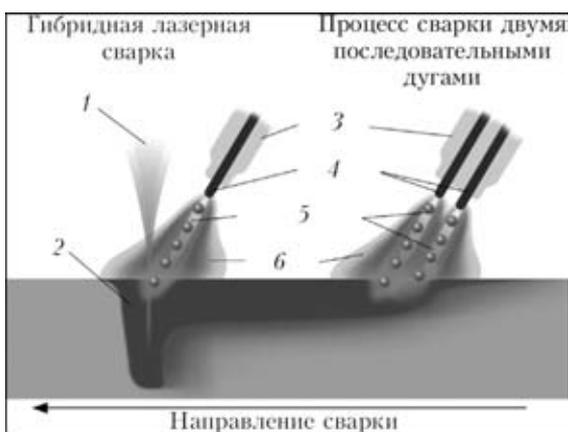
Гибридная лазерная сварка МИГ/МАГ + сварка двумя последовательными дугами (на материал воздействуют луч лазера и три дуги): 1 — луч лазера; 2 — зона сплавления; 3 — газовое сопло; 4 — электроды; 5 — импульсные дуги; 6 — защитный газ
